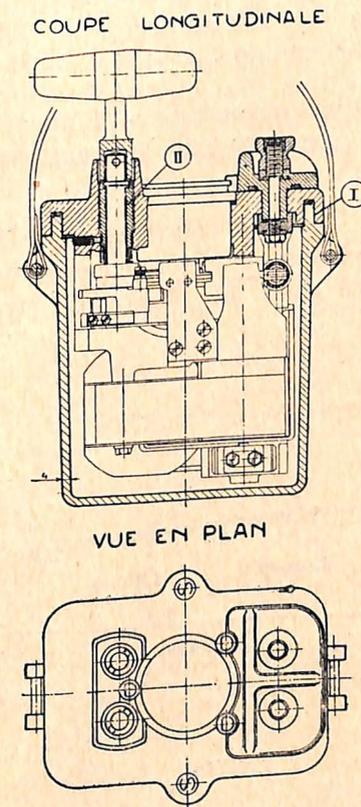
Exploseur Schaffler type A. B. F. V. S.
